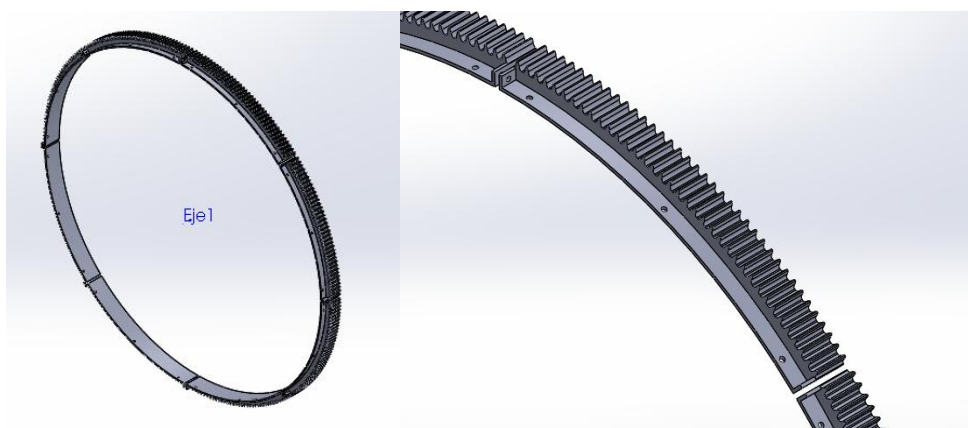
Engrane de dientes diseñado en 8 segmentos
